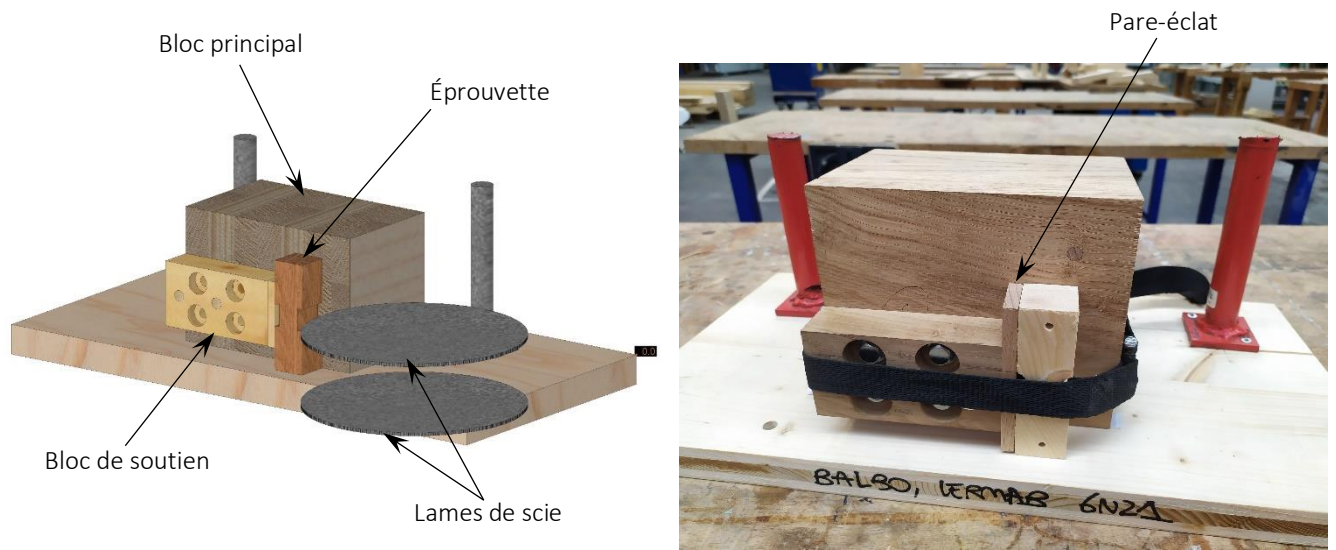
Montage d'usinage pour la découpe des blocs résiduels
